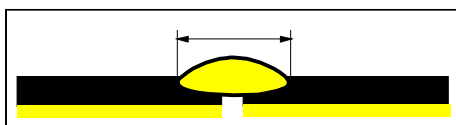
Extrusionsauftragsnaht zum Verschweißen des Ekoliners.
